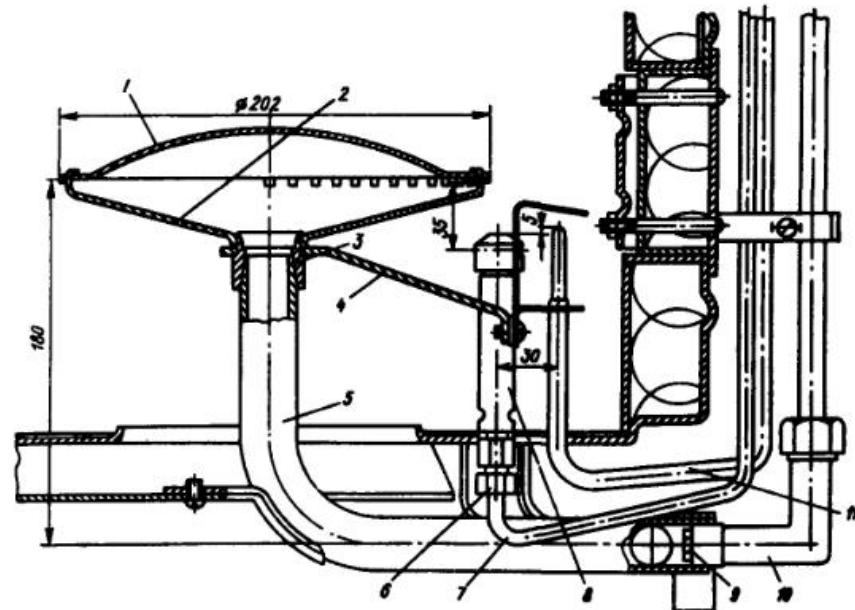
Газогорелочный узел водонагревателя АГВ-80:
